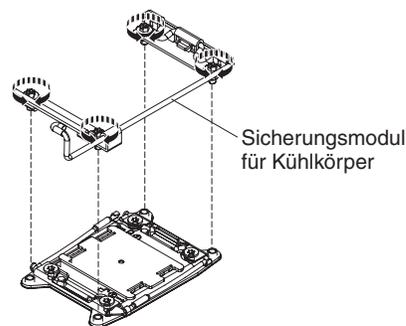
Sicherungsmodul für Kühlkörper installieren
